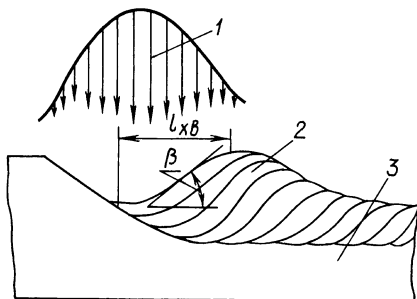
Схема сварочной ванны: 1 — сварочная дуга; 2 — слой жидкого металла; 3 — свариваемый металл
